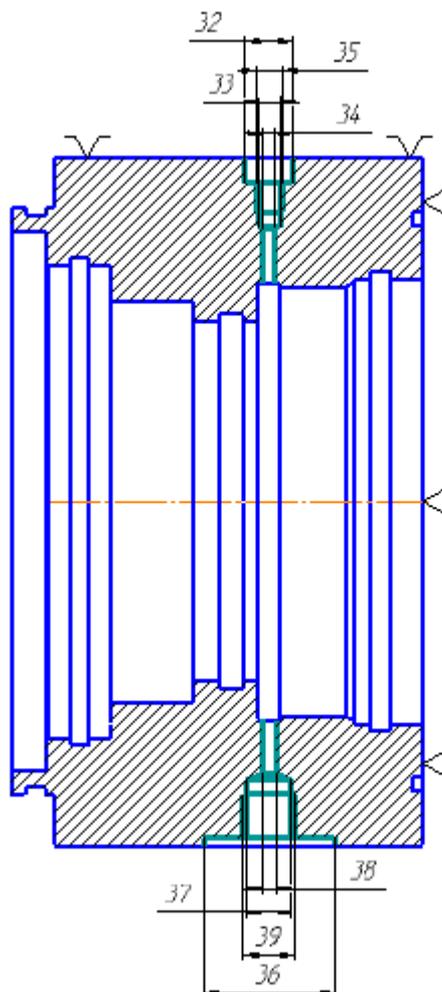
Получение отверстий на цилиндрической поверхности
